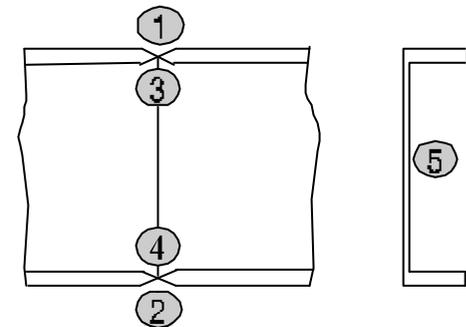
Schweißfolgeskizze
